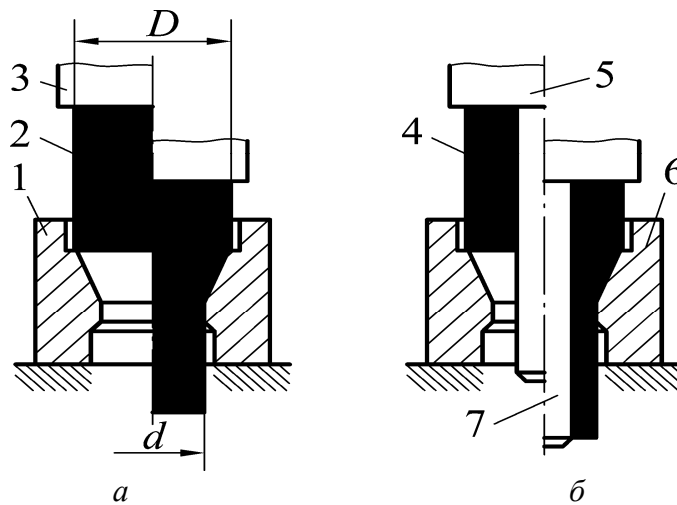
Схемы редуцирования сплошной (а) и полой (б) заготовок: 1, 6 – матрицы; 2, 4 – заготовки; 3, 5 – пуансоны; 7 – оправка; D, d – диаметры заготовки до и после редуцирования
